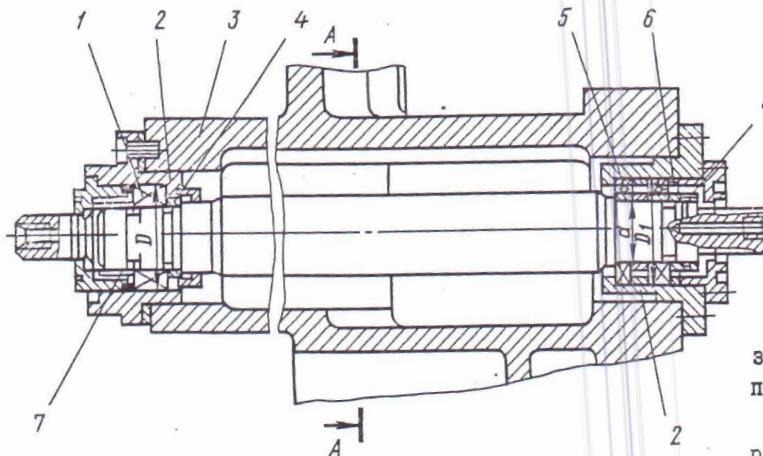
Шпиндель шлифовальной головки станка ЗЕ7IOA
